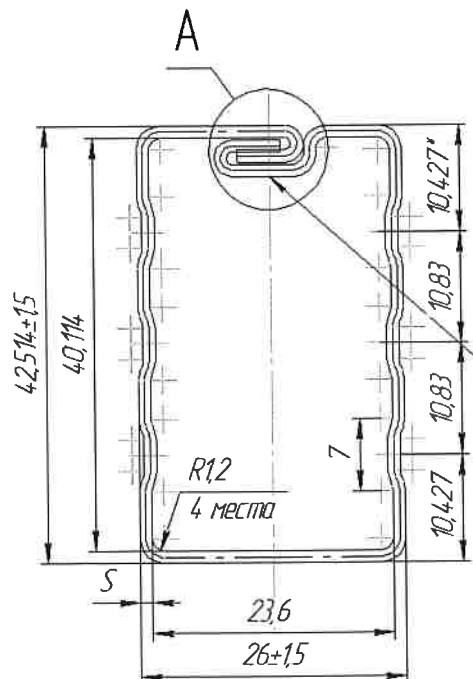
Труба с гофрами (размер заготовки 155 мм)
